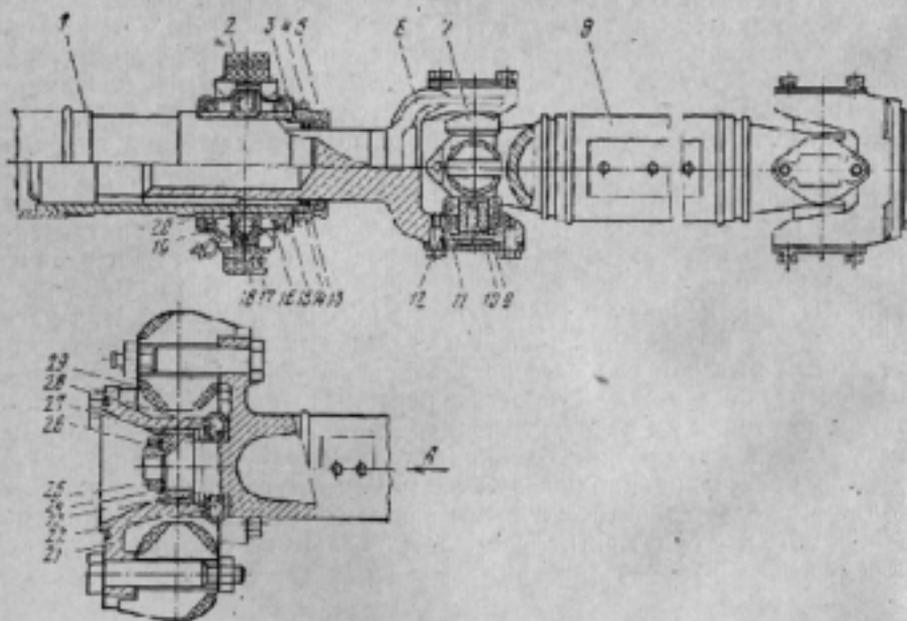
Основной карданный вал с промежуточным валом в сборе:
